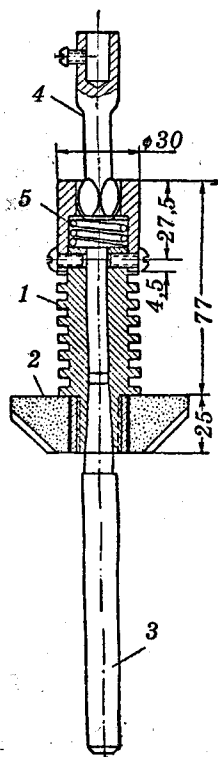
Приспособление для шлифовки гнезд абразивным наконечником:
